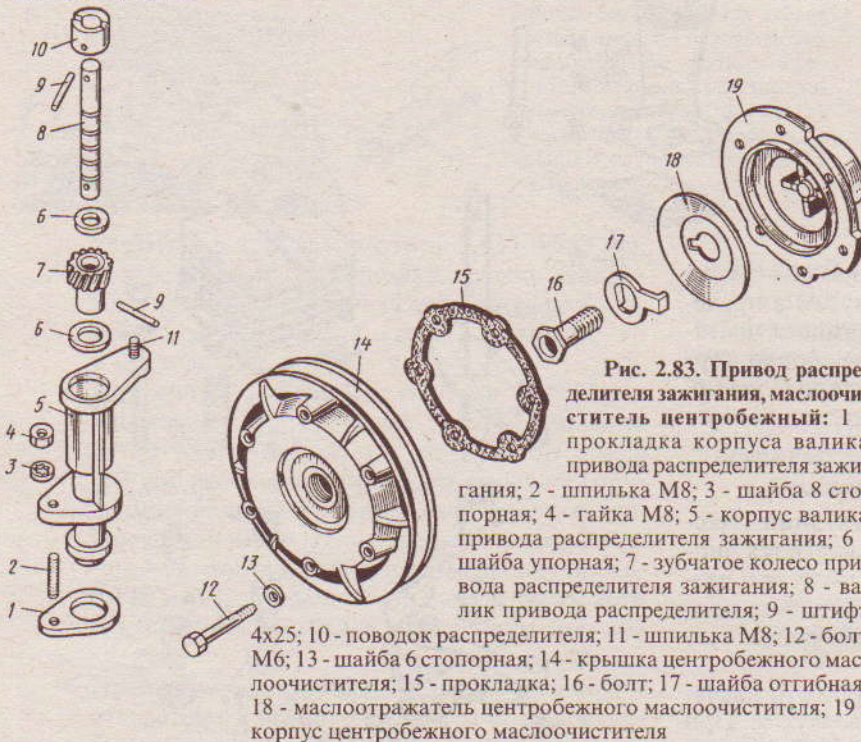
Привод распределителя зажигания, маслоочиститель центробежный: 1 - прокладка корпуса валика привода распределителя зажигания; 2 - шпилька М8; 3 - шайба 8 стопорная; 4 - гайка М8; 5 - корпус валика привода распределителя зажигания; 6 - шайба упорная; 7 - зубчатое колесо привода распределителя зажигания; 8 - валик привода распределителя; 9 - штифт 4x25; 10 - поводок распределителя; 11 - шпилька М8; 12 - болт М6; 13 - шайба 6 стопорная; 14 - крышка центробежного маслоочистителя; 15 - прокладка; 16 - болт; 17 - шайба отгибная; 18 - маслоотражатель центробежного маслоочистителя; 19 - корпус центробежного маслоочистителя
